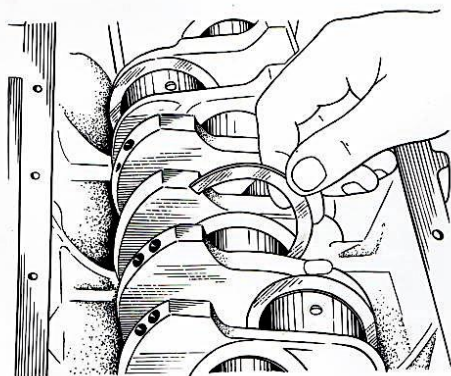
Установка упорных полуколец коленчатого вала в гнезда среднего коренного подшипника
